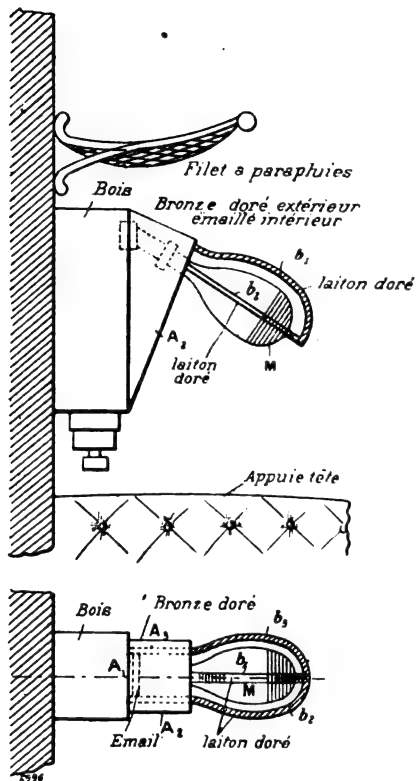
Coupe et plan d'une lampe applique de lecture (2^e disposition.)
